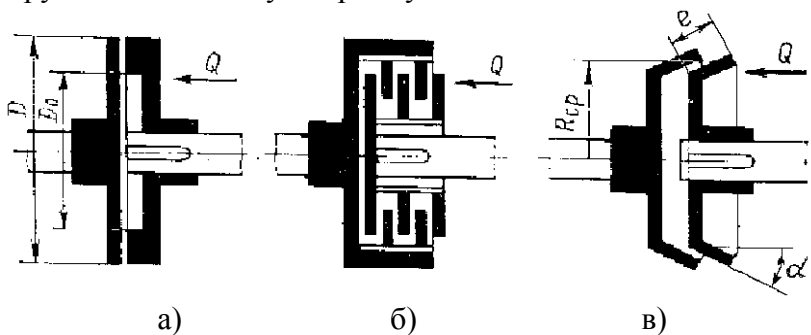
Конструкція фрикційних запобіжних механізмів:
